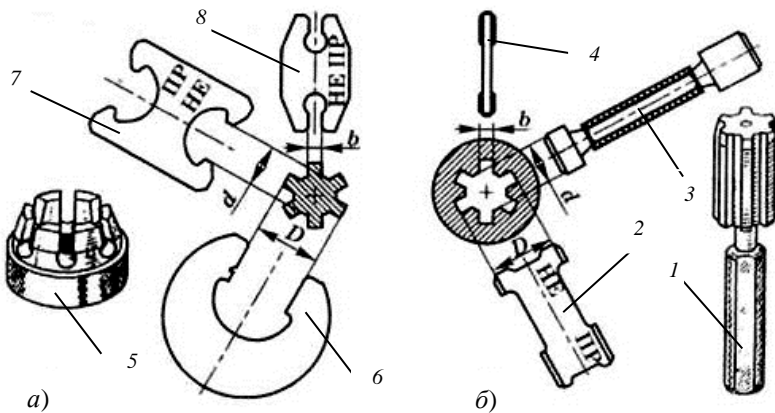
Калибры для контроля деталей шлицевого прямобочного соединения: *a* – для контроля шлицевых прямобочных валов; *б* – для контроля шлицевых прямобочных втулок; 1 – комплексный проходной калибр-пробка; 2 – неполный калибр-пробка для контроля параметра *D*; 3 – полный гладкий калибр-пробка для контроля параметра *d*; 4 – неполный непроходной калибр-пробка для контроля ширины пазов *b*; 5 – комплексный калибр-кольцо проходной; 6 – калибр-скоба для контроля параметра *D*; 7 – калибр-скоба для контроля параметра *d*; 8 – калибр-скоба для контроля толщины шлица *b
